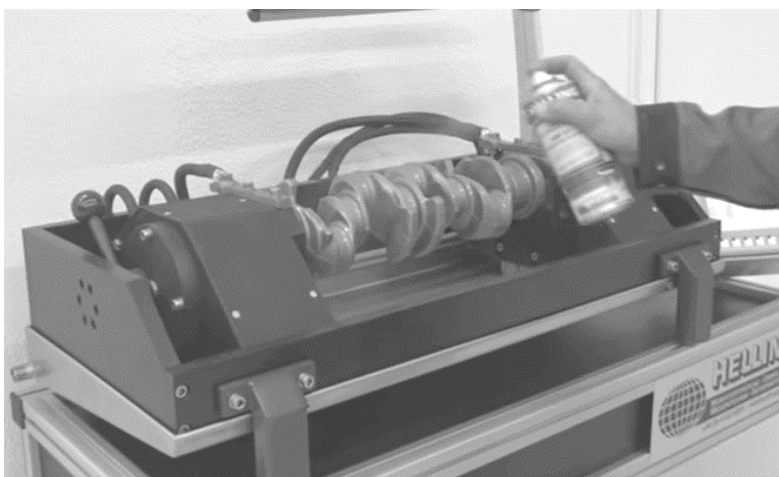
Магнітно-порошковий дефектоскоп Universal 450 [12]
